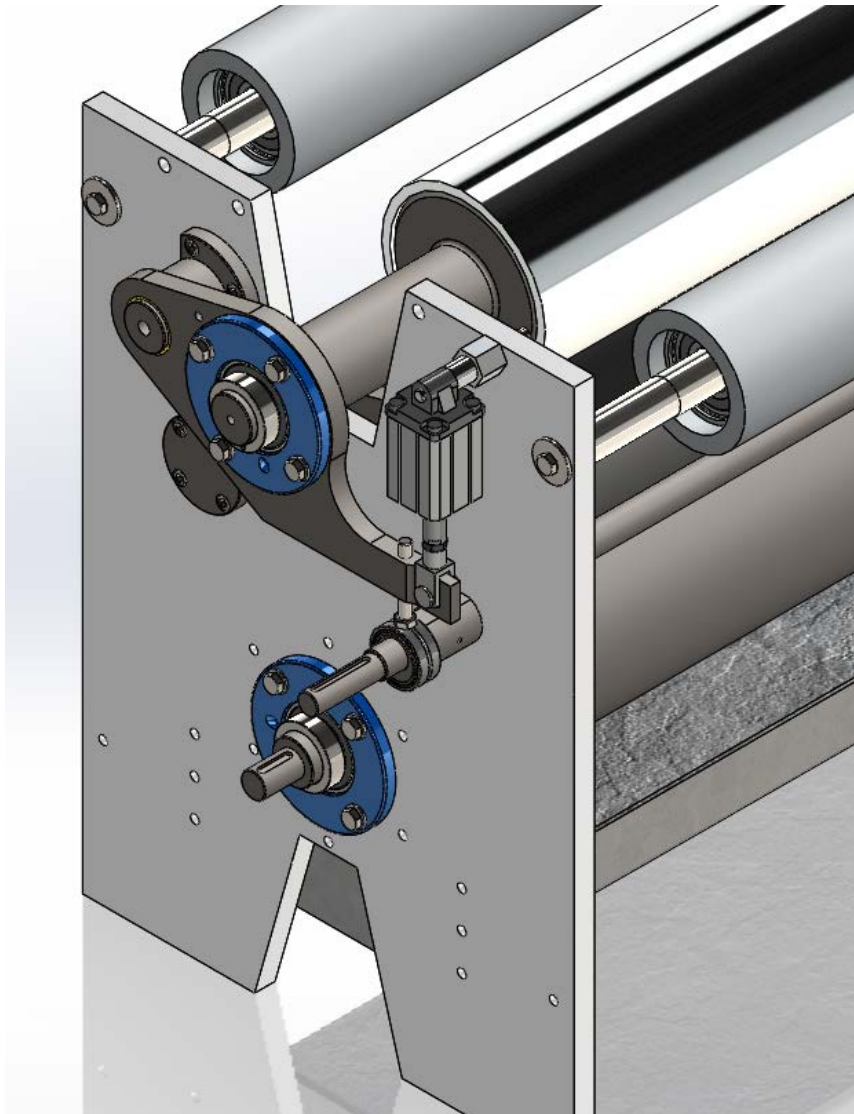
Ensamblaje de piezas
